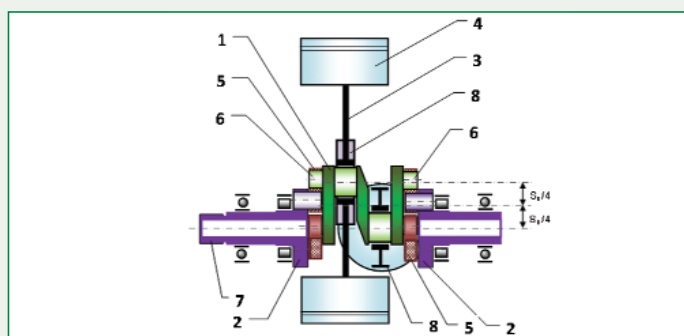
Схема бесшатунного механизма в варианте Б для четырёхцилиндрового двигателя: 1 - план-шайба торца планетарного коленчатого вала (ПКВ); 2 - план-шайба центрального опорного вала; 3 - поршневой шток; 4 - поршень; 5 - межосевые элементы (серги) 3+3; 6 - силовые пальцы; 7 - выходной конец центрального опорного вала; 8 - ползун
